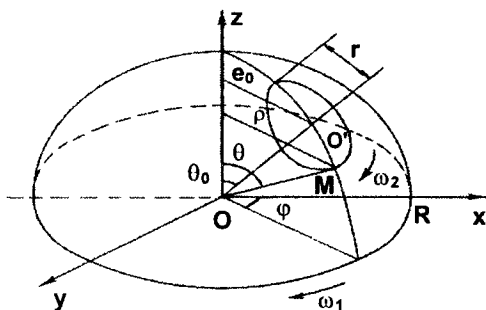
Схема обробки сферичної поверхні оптичної деталі
